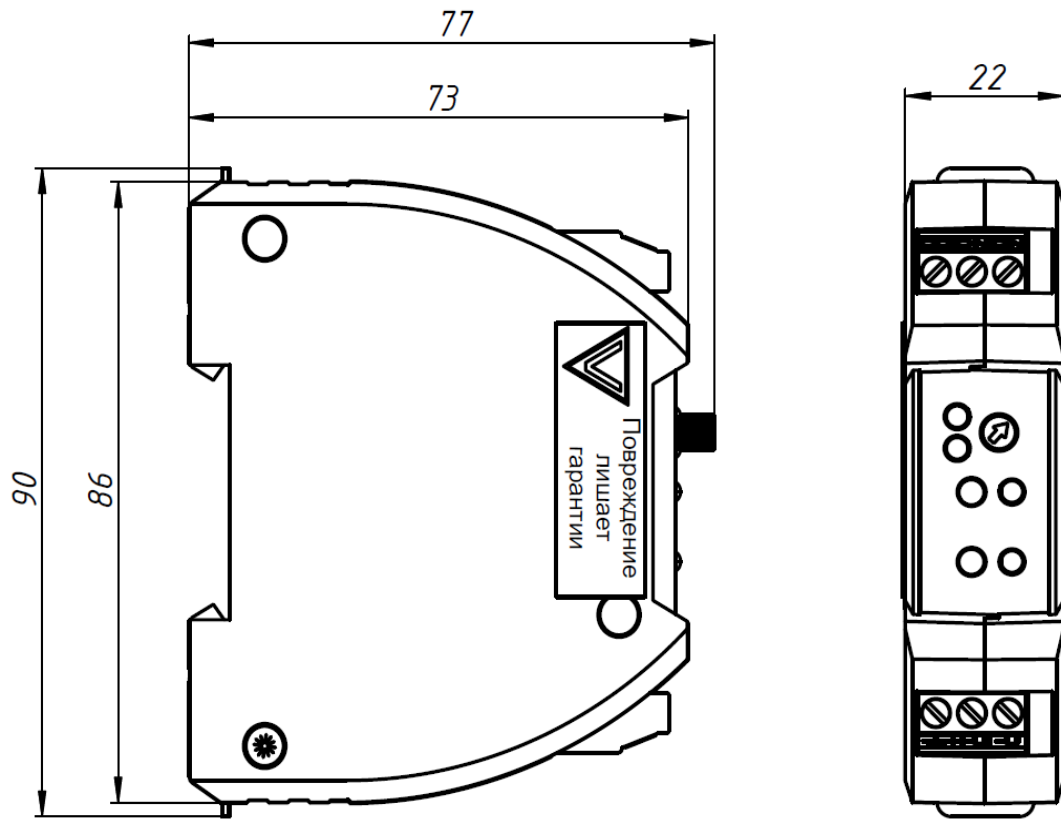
Внешний вид. Габаритный чертёж РКСИ-1001
